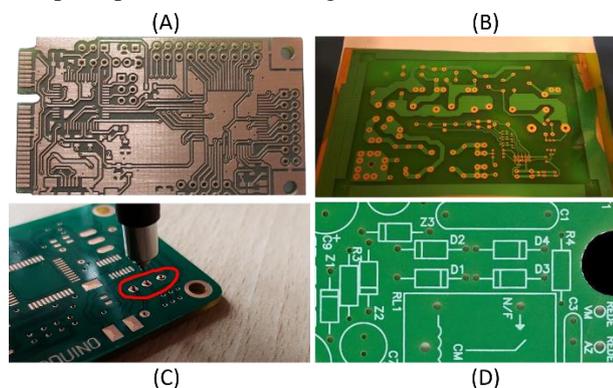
Processo completo. (A) – Fresagem, (B) – máscara de solda, (C) – Metalização de furos, (D) – Legenda dos componentes.
